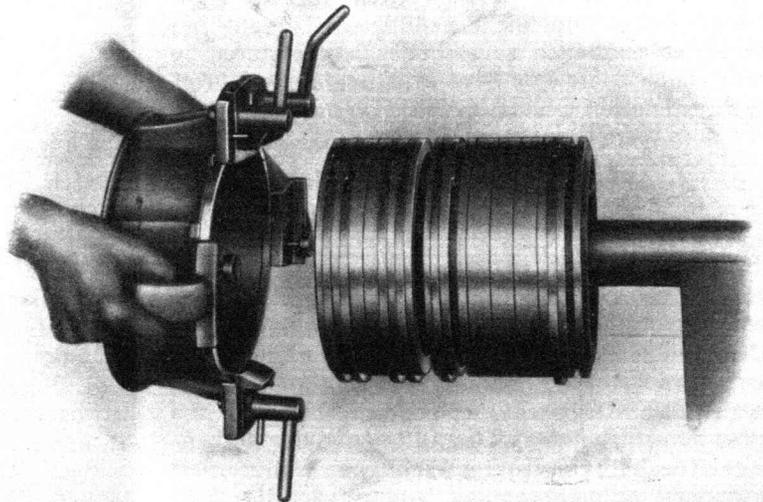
Aufbringen des Ringes auf den Kolben mittels der Knorr-Aufziehvorrichtung.
